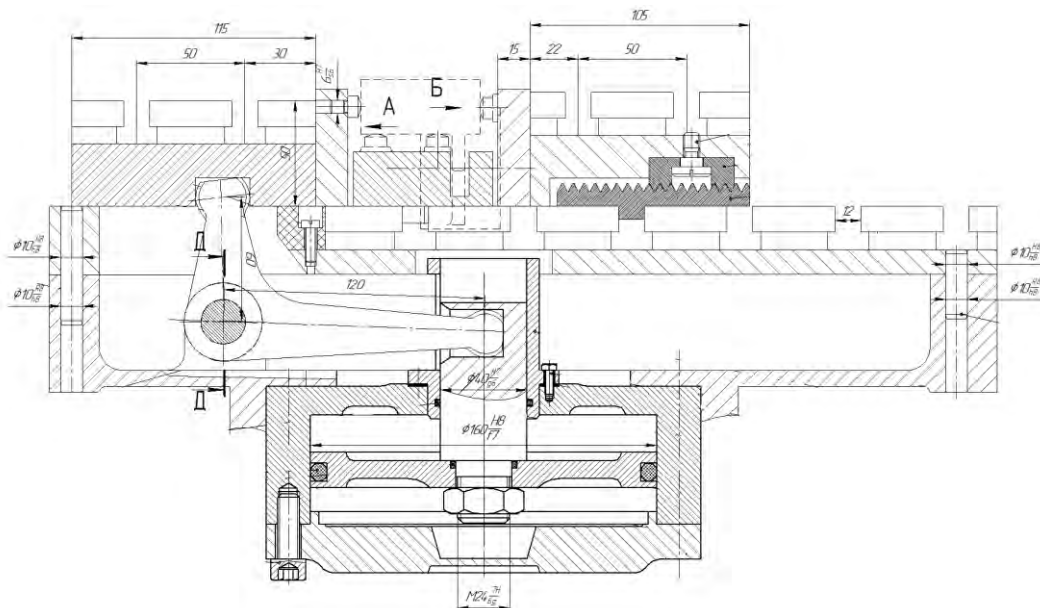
Эскиз установочно-зажимного приспособления.
